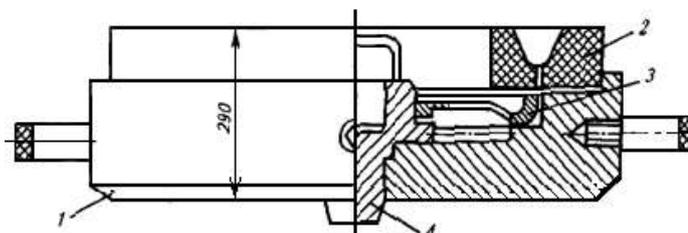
Схема кокиля для восстановления ведущего колеса заливкой жидким металлом:
